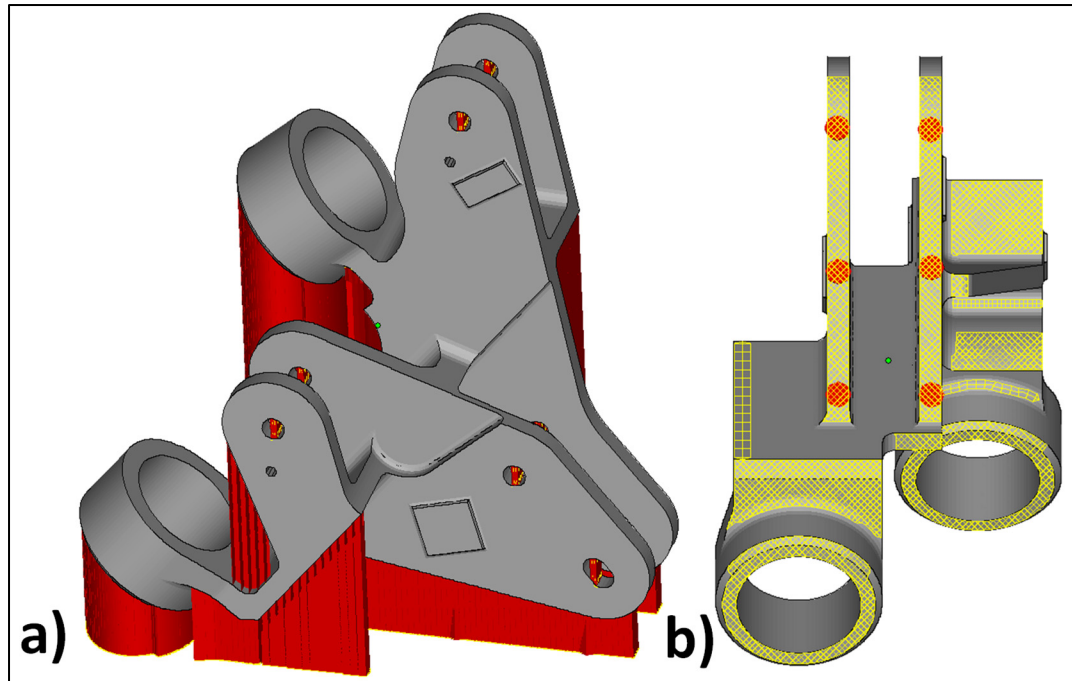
Pièce avec supports : a) Vue iso; b) Vue du dessous
